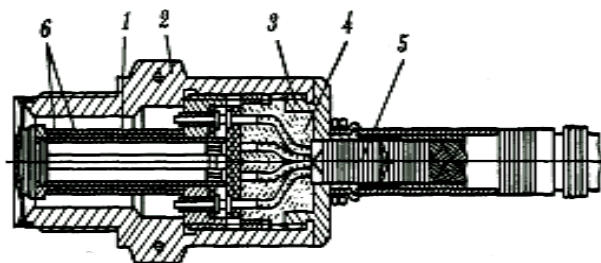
Тензорезистивный датчик давления: 1 – упругий элемент; 2 – корпус; 3 – хвостик корпуса; 4 – заливка датчика; 5 – кабельная перемычка; 6 – тензорезисторы
